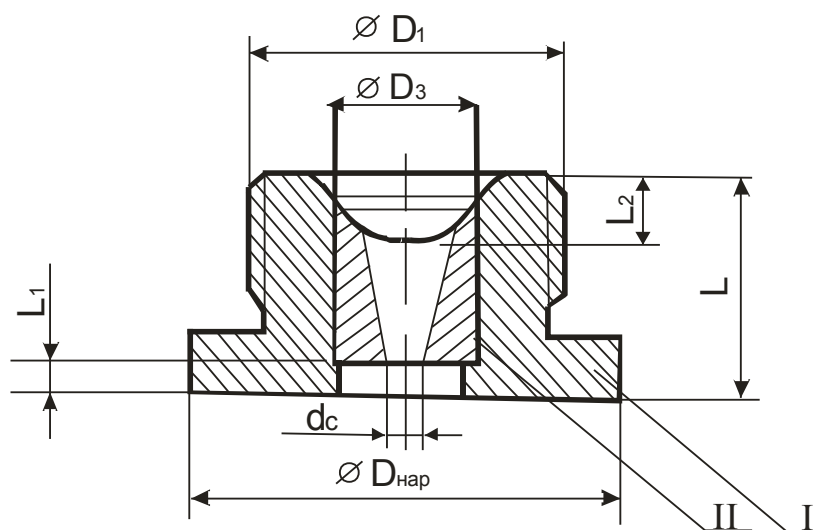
Схема корпуса насадки с твердосплавной винтовой вставкой.
